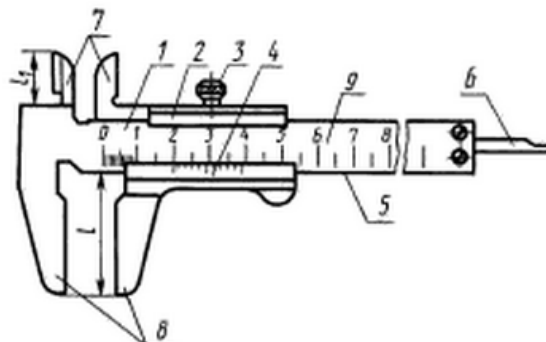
Штангенциркуль двусторонний с глубиномером
